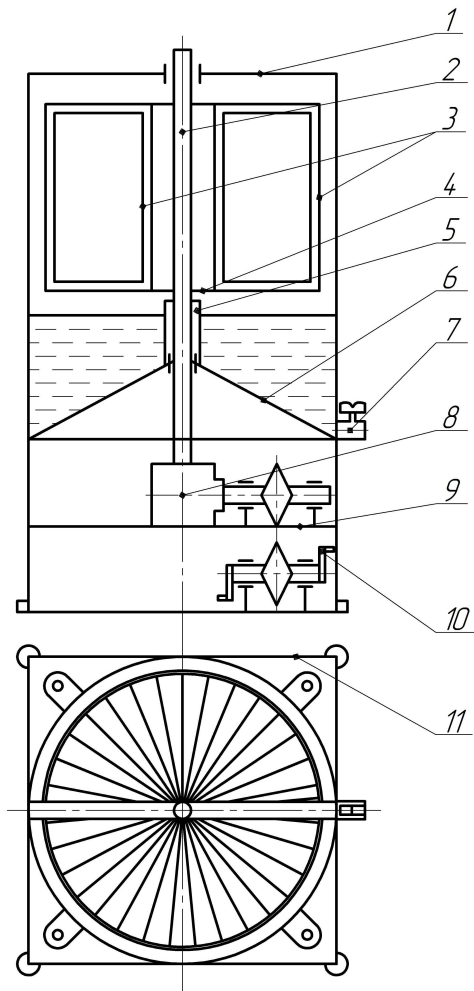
Схема нової ножної медогонки: 1- стальна планка для підтримки вала; 2- вал; 3- рамки; 4- ротор медогонки; 5- обсадна труба; 6- бак; 7-кран; 8- конічна прямозуба передача; 9- металева планка для кріплення; 10- ланцюгова передача; 11- металевий стіл під медогонку
